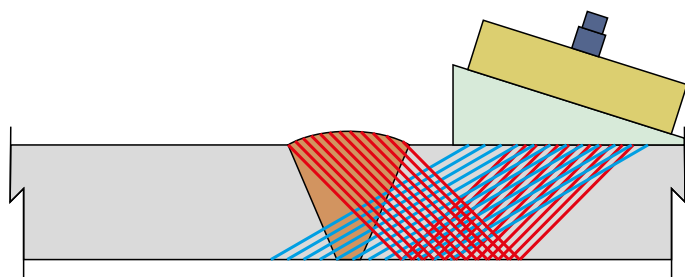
Схемы контроля сварного шва с помощью ФР
